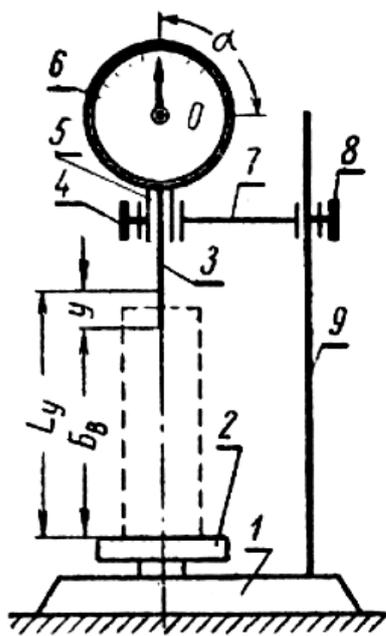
Принципиальная схема стойки и установленного на ней индикатора (прибора):
